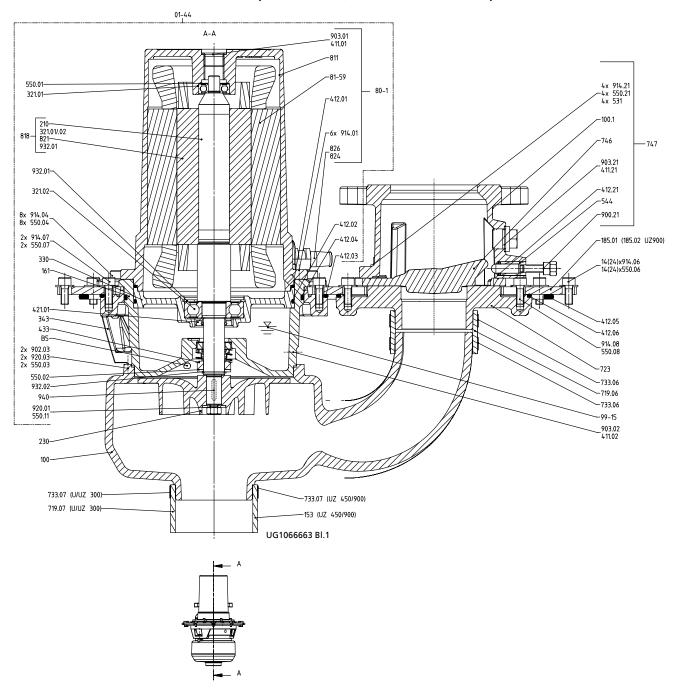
Disegno complessivo Compacta U100/300, UZ150/300, UZ 450/900 - parte rotante
